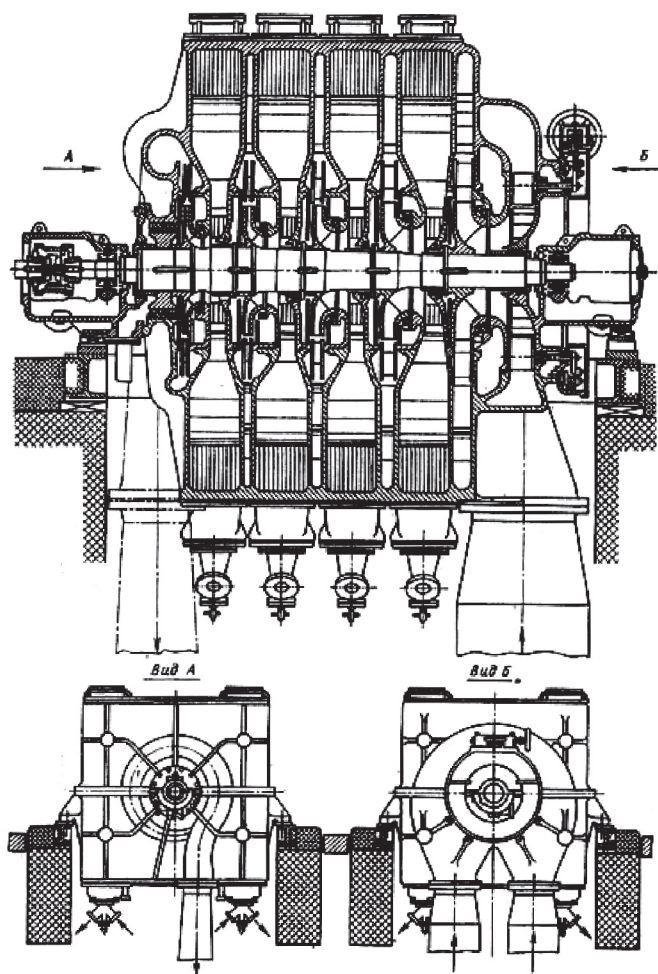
Центробежный компрессор фирмы «Броун-Бовери»
